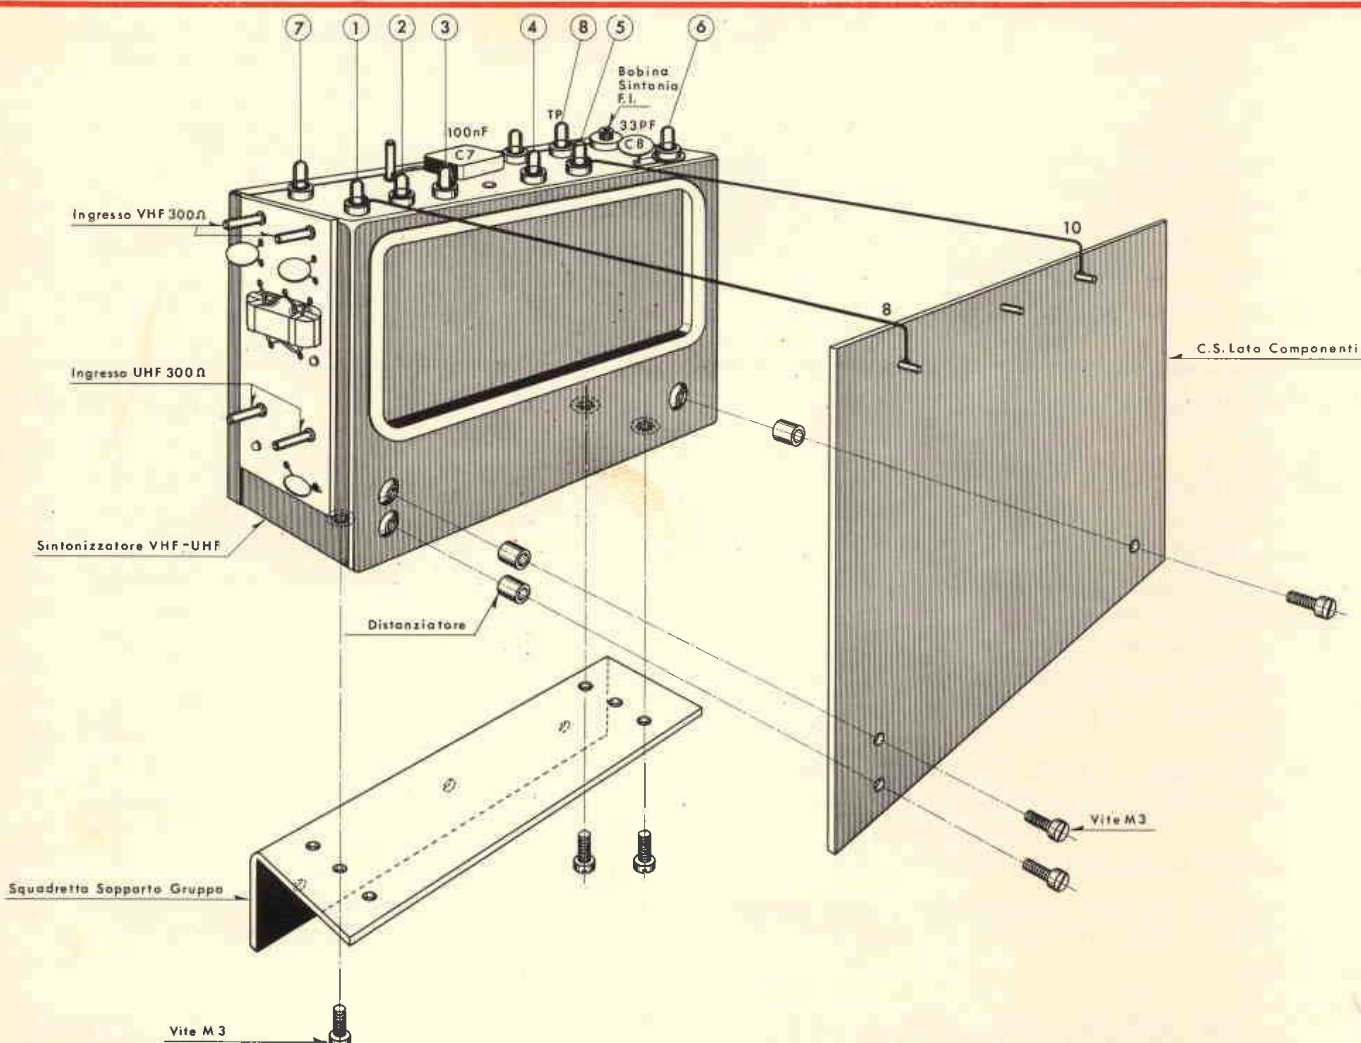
Esploso di montaggio del circuito stampato al sintonizzatore.
